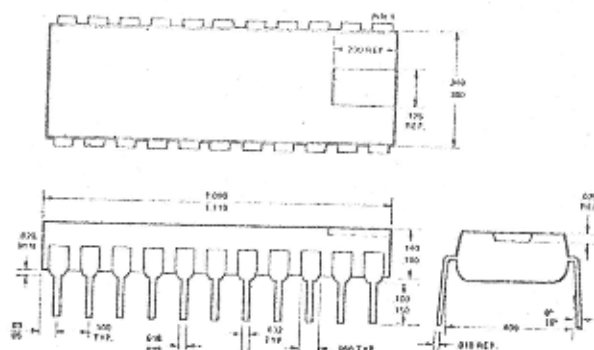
Схема 22-штырькового пластикового корпуса с двухсторонним расположением выводов/P/
